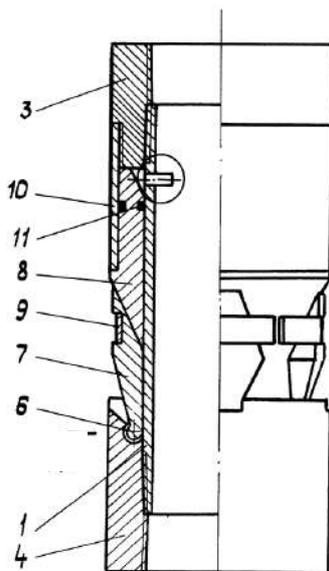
Центратор гидравлический [2]: 1 – обсадная труба; 2 – отверстия; 3, 4 – муфты; 5 – кольцевая канавка; 6 – оси; 7 – рычаги; 8 – рабочий поршень; 9 – разрезное пружинное кольцо; 10 – цилиндр; 11 – резиновые кольца
